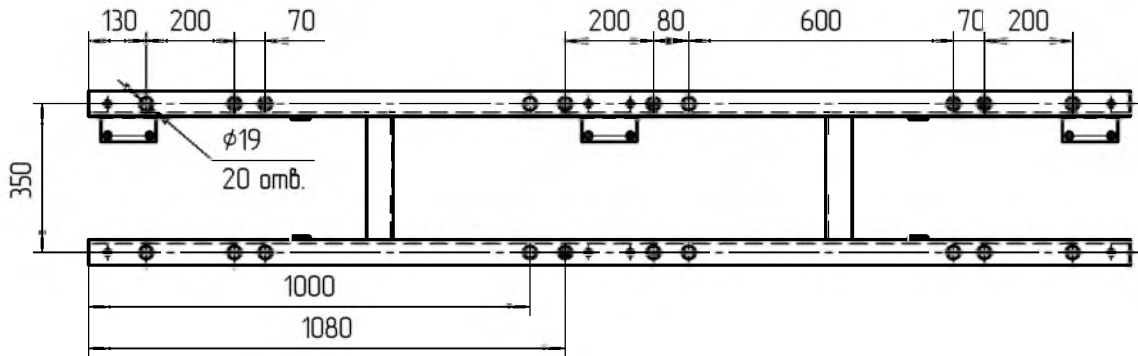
Разметка присоединительных отверстий на общей раме разъединителя
